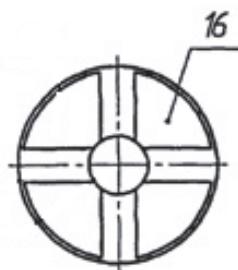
Стопорная контргайка для промывочной насадки (вид снизу)
